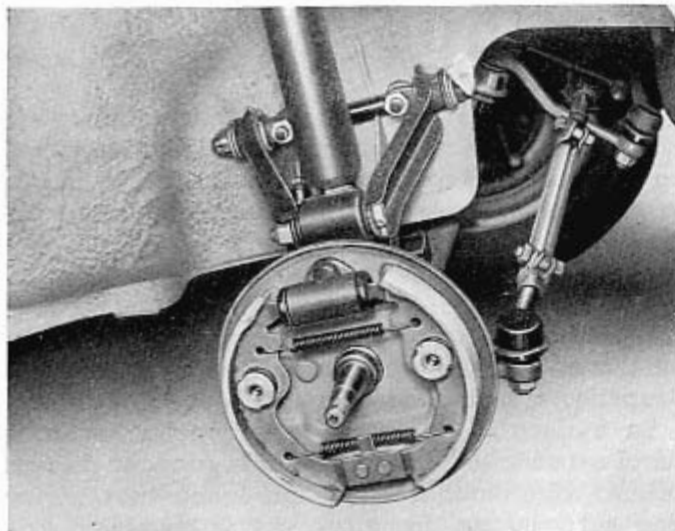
Plateau de frein de roue avant droite, sans tambour.
